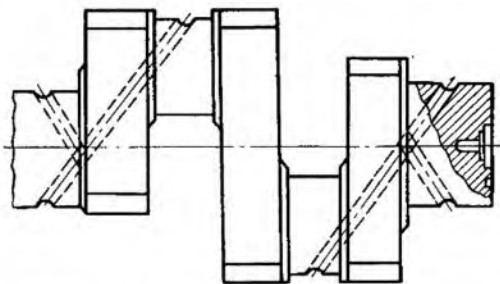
Коленчатый вал компрессора со встречным движением поршней
